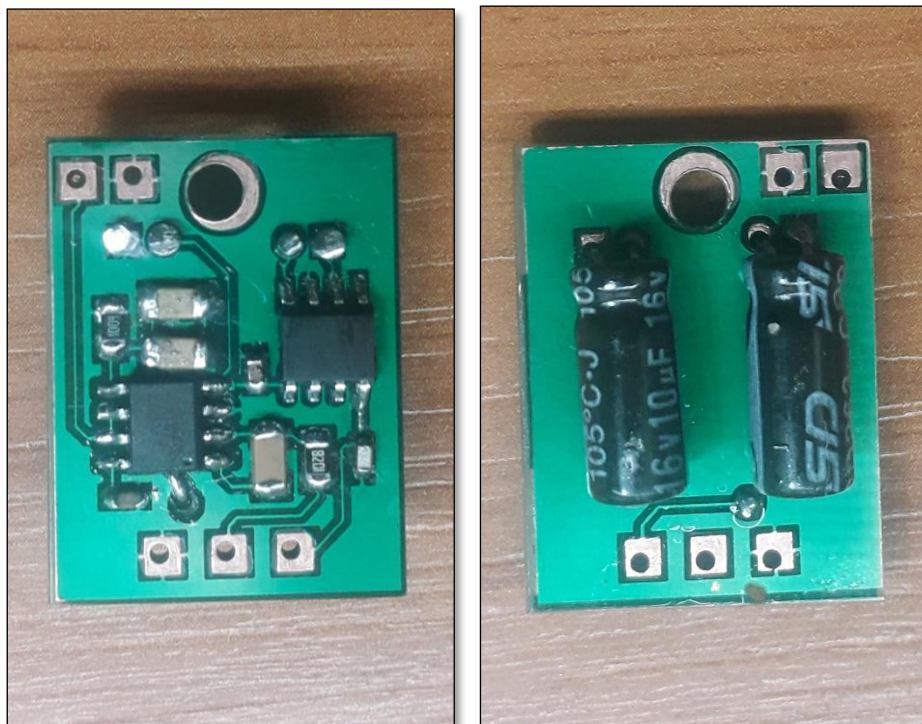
PCB de Bobina Rogowski con componentes soldados
